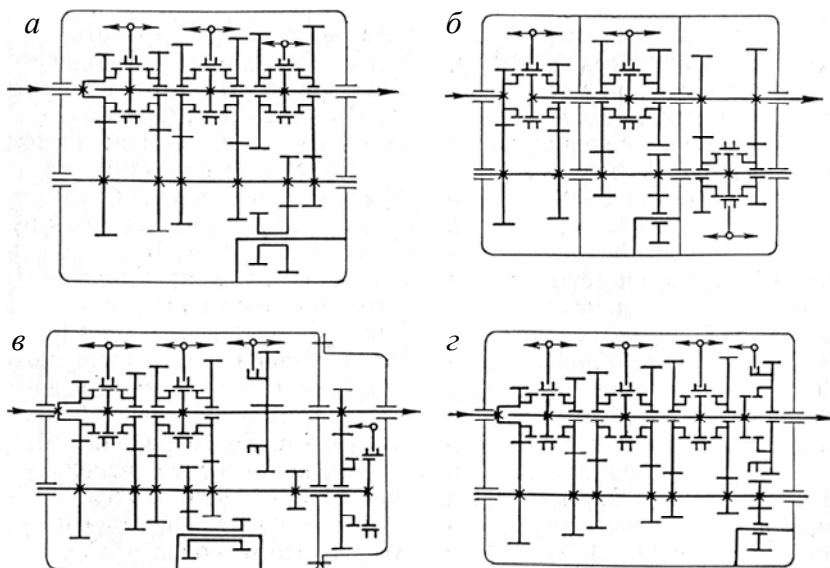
Схемы трехвалных коробок передач с соосным расположением входного и выходного валов:
